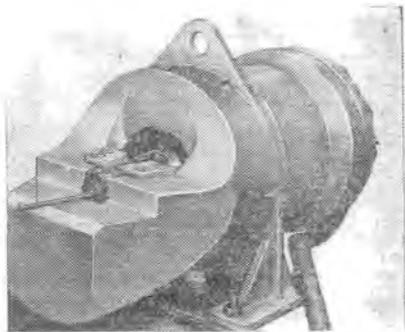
Гидропресс для образования на проволоках анкерных головок
